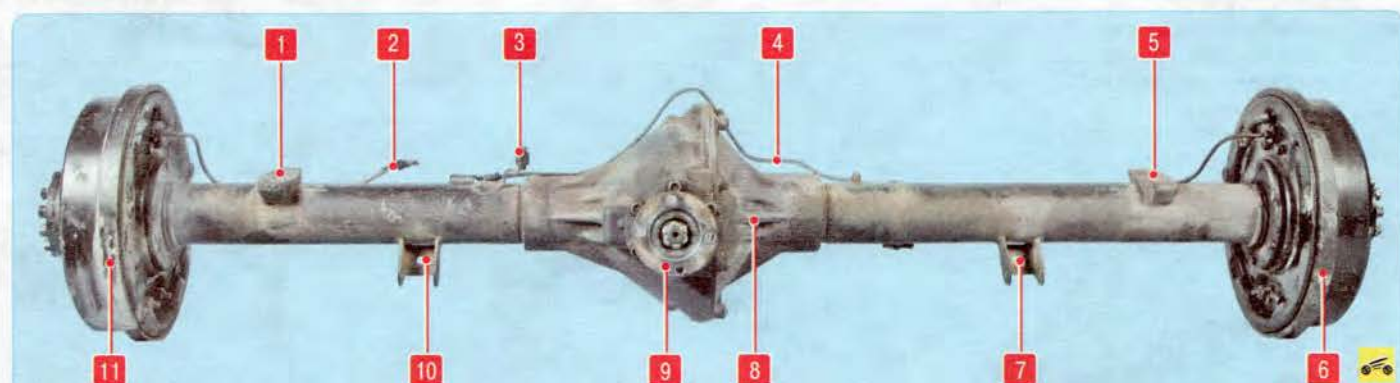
Задний мост с разъемным картером: 1, 5 – места установки подкладок рессор; 2 – трубка тормозного механизма правого заднего колеса; 3 – кронштейн крепления стойки рычага привода регулятора давления задних тормозов; 4 – трубка тормозного механизма левого заднего колеса; 6, 11 – тормозные механизмы задних колес; 7, 10 – кронштейны крепления нижних концов задних амортизаторов; 8 – картер; 9 – фланец ведущей шестерни
